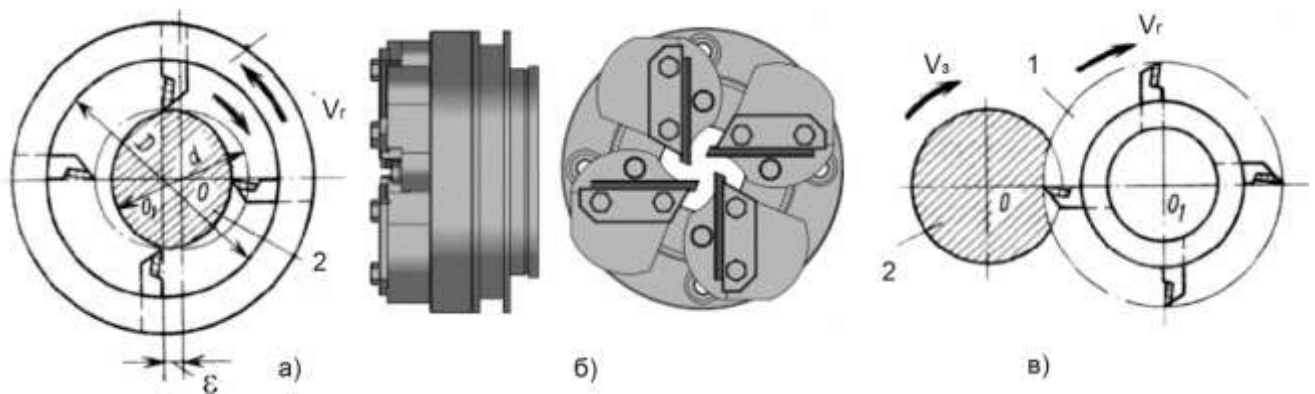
Схеми чотирирізцевої головки: а – для внутрішнього торкання; б-зовнішній вигляд головки; в – для зовнішнього торкання.
